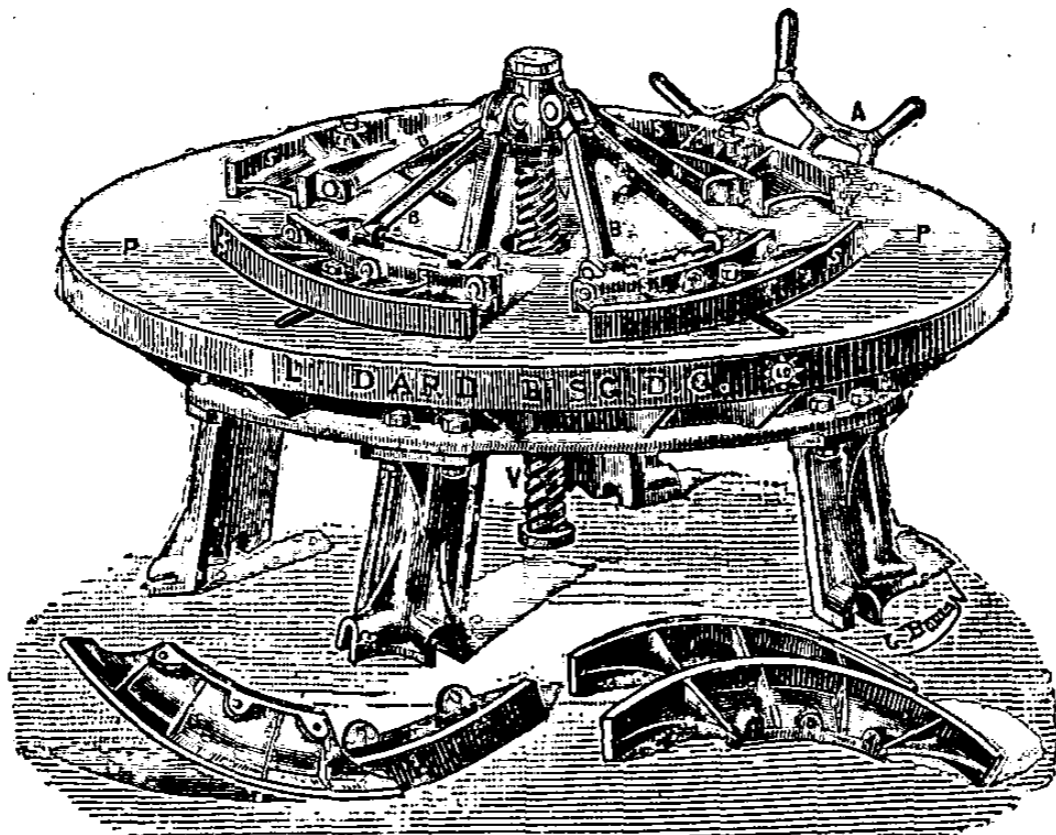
Machine à arrondir et à dégauchir les cercles.
